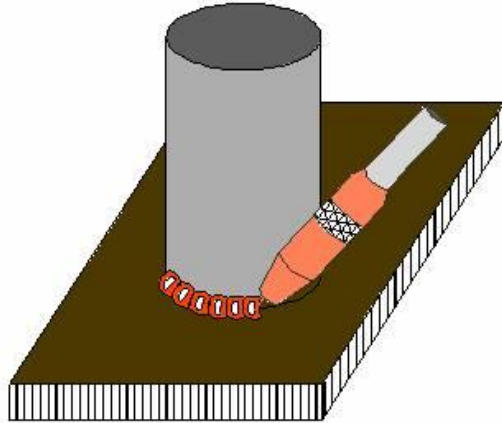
Unión de soldadura de tubo y chapa
